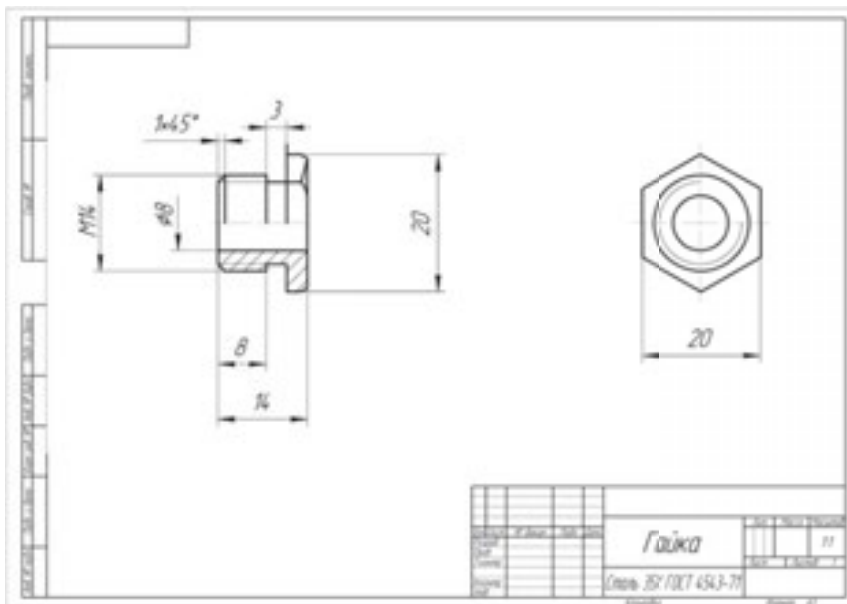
Уточненный рабочий чертеж детали «Гайка»
